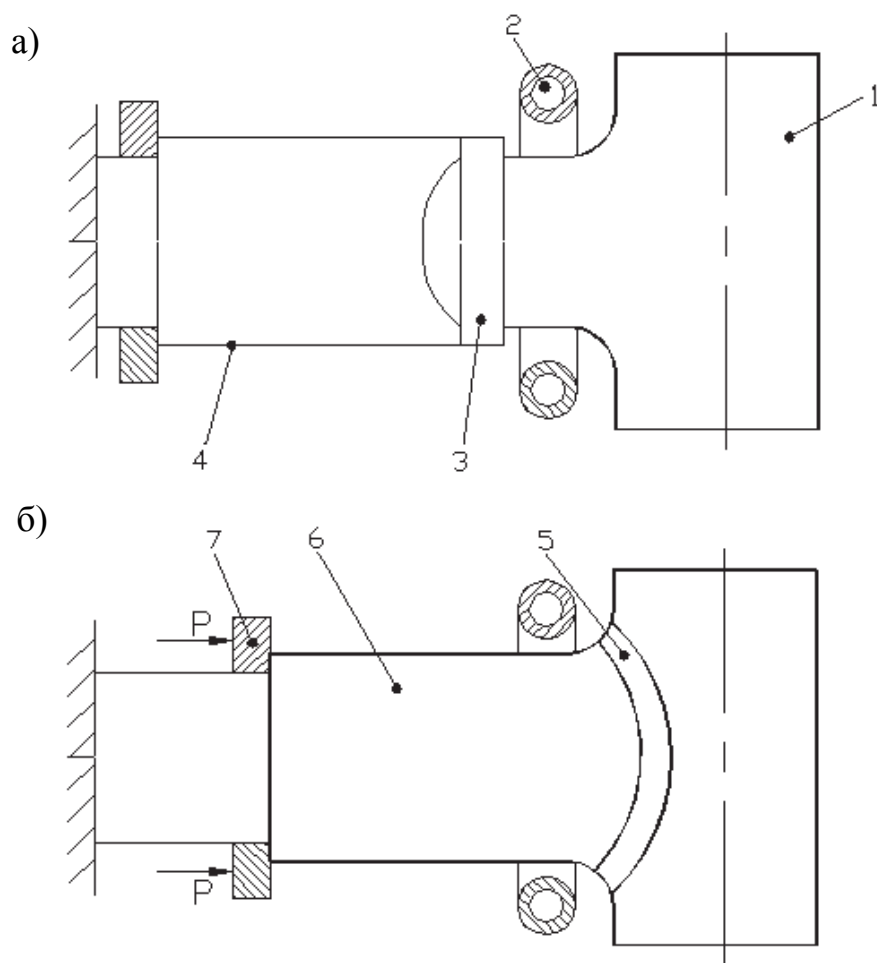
Схема изготовления фланца раздачи на конце трубы:
